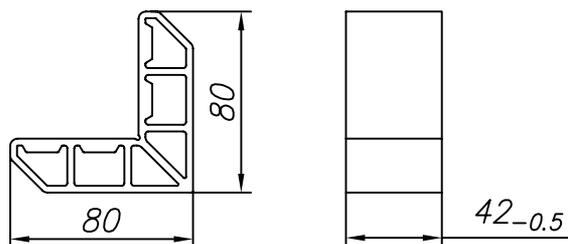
Изготовление соединителя углового FLGU.400.0914
